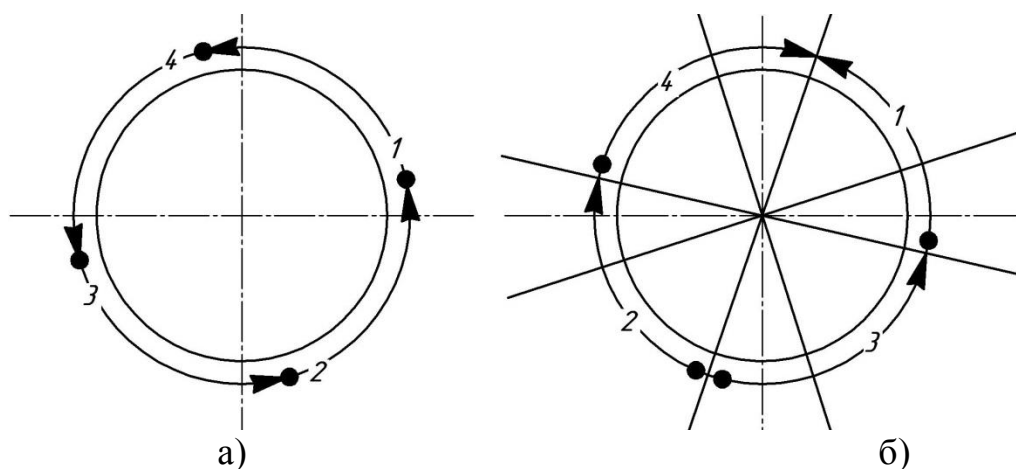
Порядок сварки участков корневого слоя шва при сварке горизонтального (а) и вертикального (б) стыка труб
